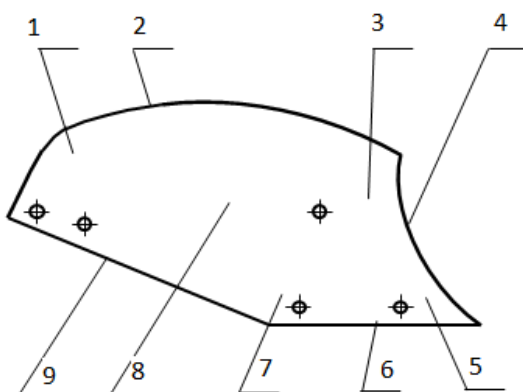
Схема конструкции областей отвала 1-крыло; 2-верхний обрез; 3-грудь; 4-полевой обрез; 5-носок; 6-стыковой обрез; 7-пятка; 8-рабочая поверхность; 9-бороздной обрез.
